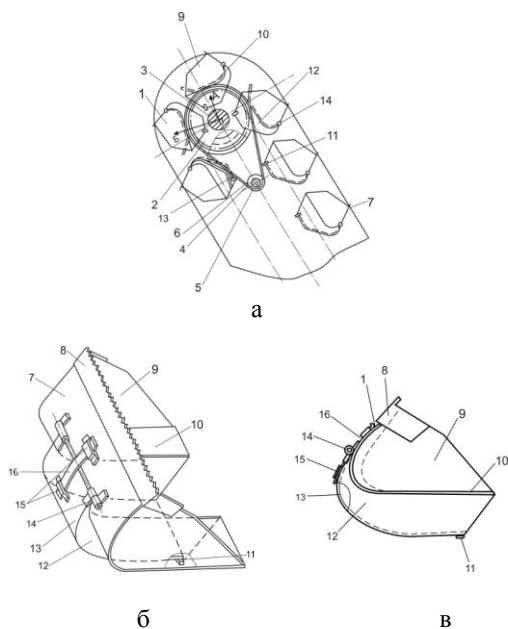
Ковшовый элеватор с ковшами с подвижными днищами изогнутой формы: 1 – углубленные ковши; 2 – звездочки, жестко закрепленные на приводном валу; 3 – приводной вал; 4 – звездочки, установленные на дополнительной оси; 5 – дополнительная ось; 6 – дополнительная цепь; 7 – верхняя стенка; 8 – гребенка с зубьями; 9 – боковые стенки; 10 – нижняя стенка; 11 – упор; 12 – вертикальные ребра; 13 – подвижное днище; 14 – петли; 15 – скобы; 16 – плоская пружина
